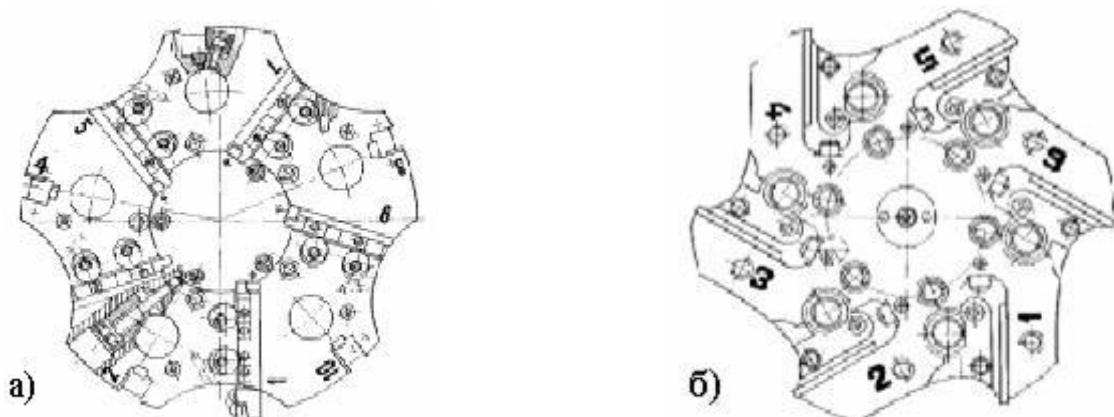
Револьверні головки: а – п'ятипозиційна, б – шестипозиційна
